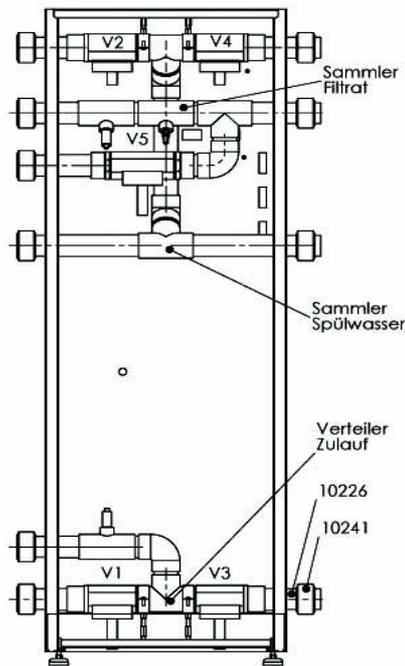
Rückansicht des Steuermoduls mit Aktoren und Sensoren
